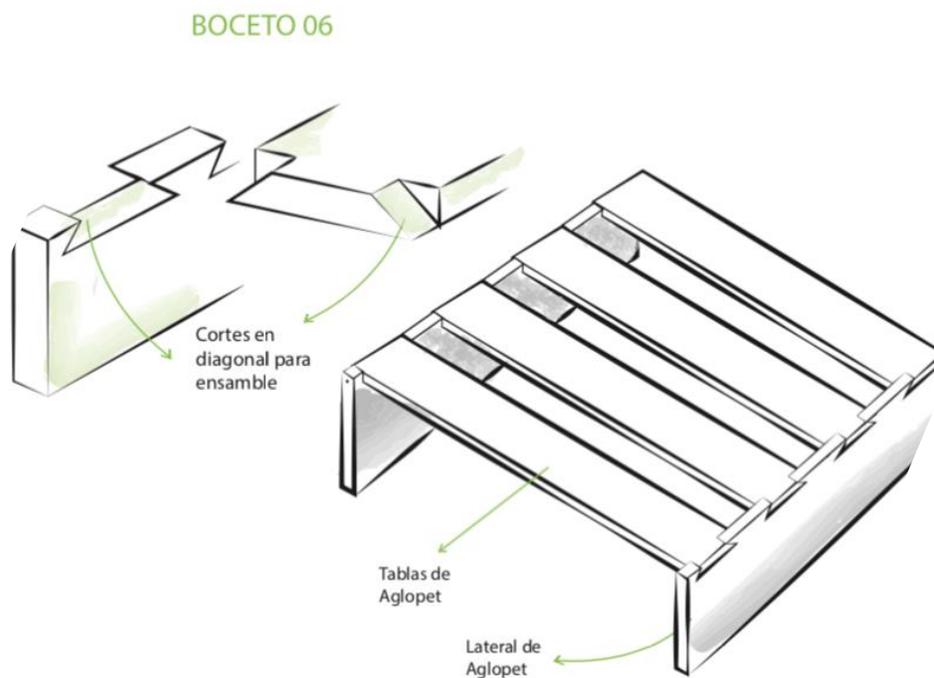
Dibujo técnico alternativa 05. Fuente: La Autora.
